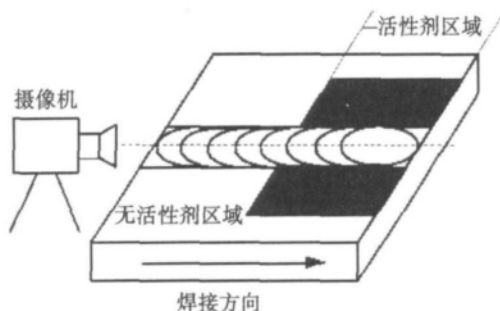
镁合金 AZ31B 试样 TIG/A-TIG 焊接示意图
